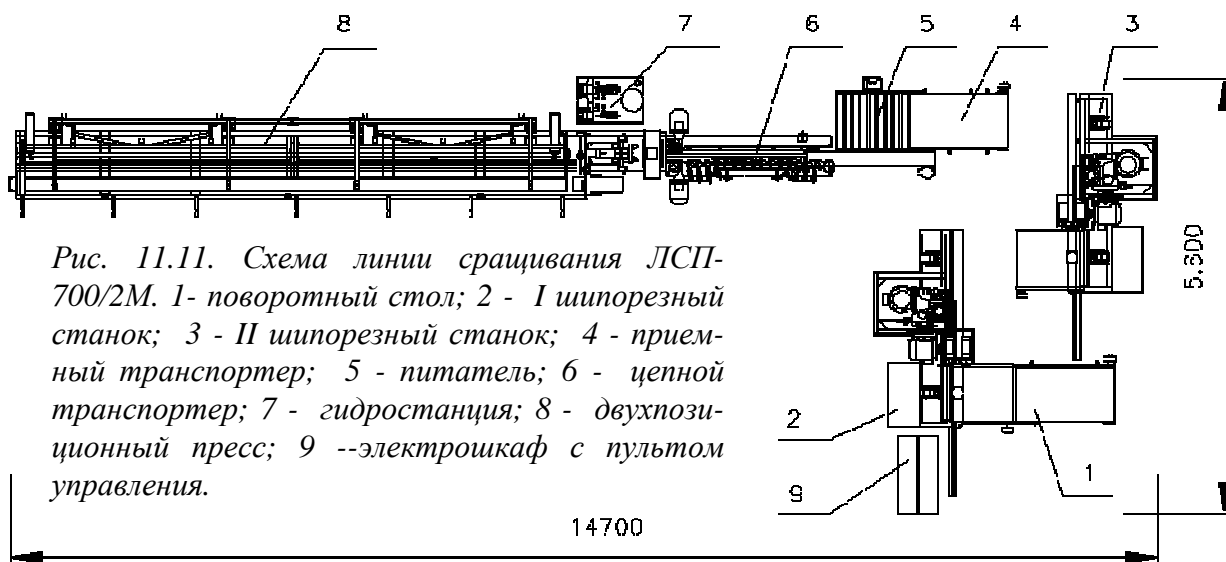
Схема линии сращивания ЛСП-700/2М. 1- поворотный стол; 2 - I шипорезный станок; 3 - II шипорезный станок; 4 - приемный транспортер; 5 - питатель; 6 - цепной транспортер; 7 - гидростанция; 8 - двухпозиционный пресс; 9 --электрошкаф с пультом управления.
